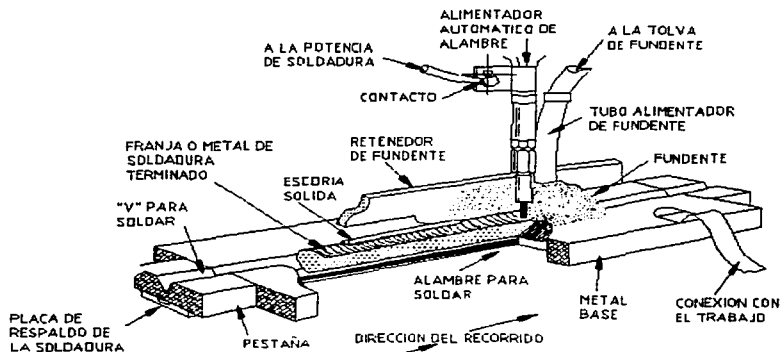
Proceso de soldadura por arco sumergido.
